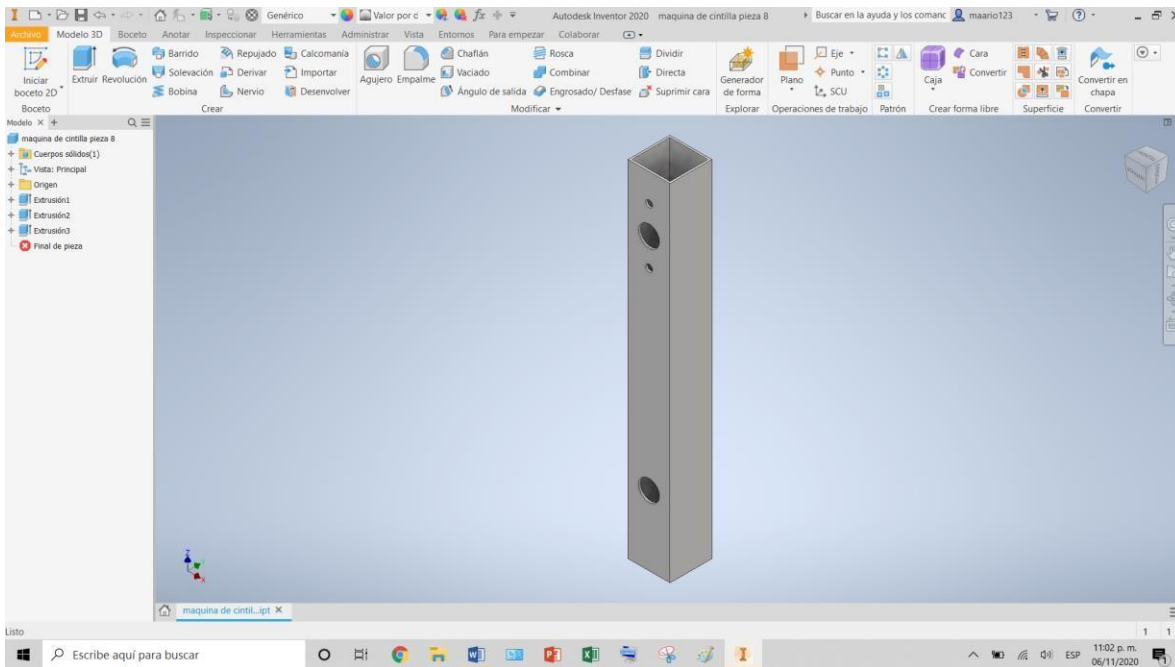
plano de la pieza número siete para máquina de cintilla.
